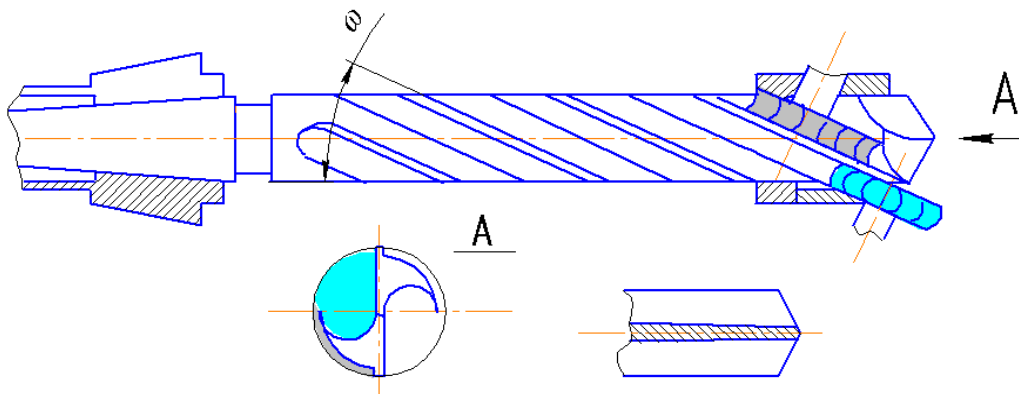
Схема одночасної обробки канавки та спинки свердла
